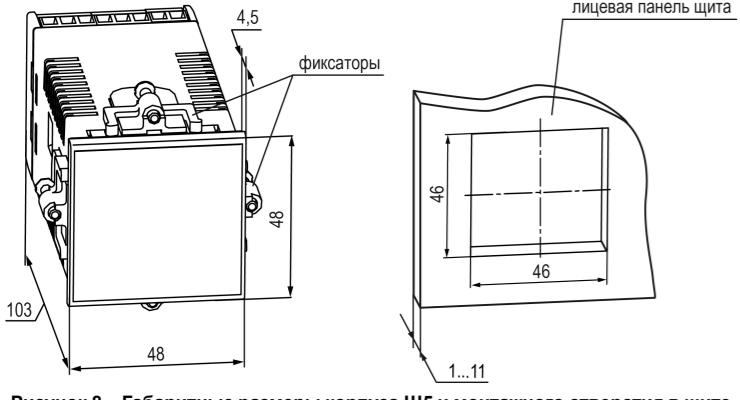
Габаритные размеры корпуса Щ5 и монтажного отверстия в щите
